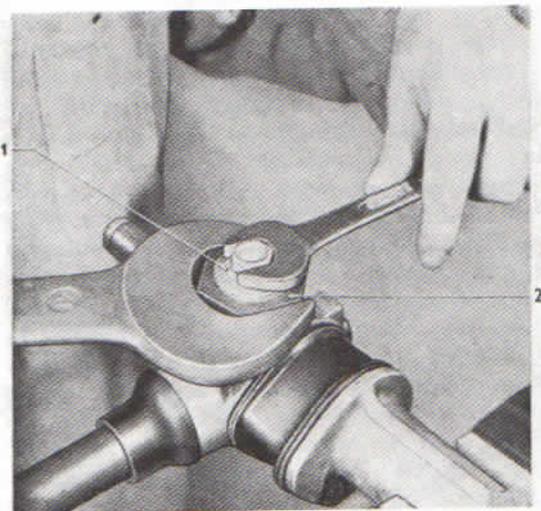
Sechskant-Gegenmutter für Einstellschraube lösen (am ausgebauten Lenkgetriebe – ohne Spurstangen – gezeigt)
